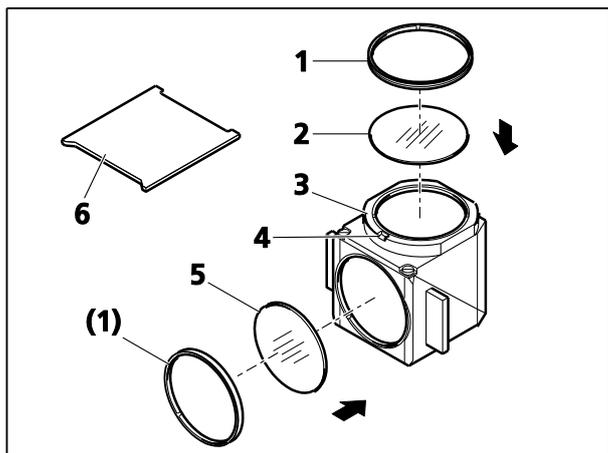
Remplacement du jeu de filtres dans le module réflecteur FL P&C
